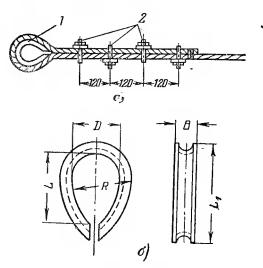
Коуш. а → размещение коуша в тросе; б — основные размеры.
